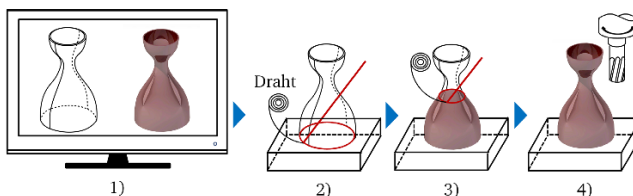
Funktionsprinzip der drahtbasierten Prozesse: CAD-Modell des Bauteils, 2) Schmelzen des Drahtes, 3) Anheben des Auftragsschweißkopfes und Auftrag einer neuen Schmelzbahn, 4) Bearbeitung des Bauteils
